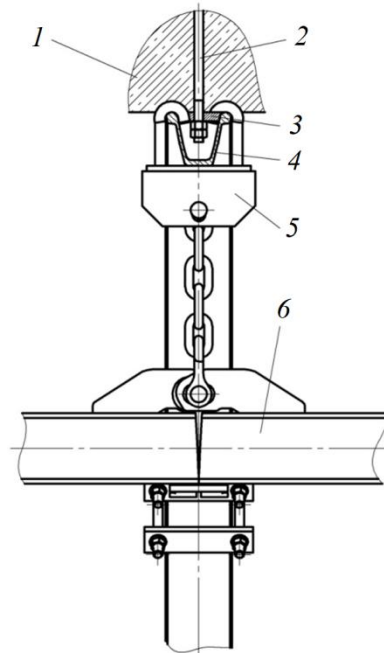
Общий вид конструкции анкерного соединения для предотвращения смещения крепи при торможении ПС ШПМД:
